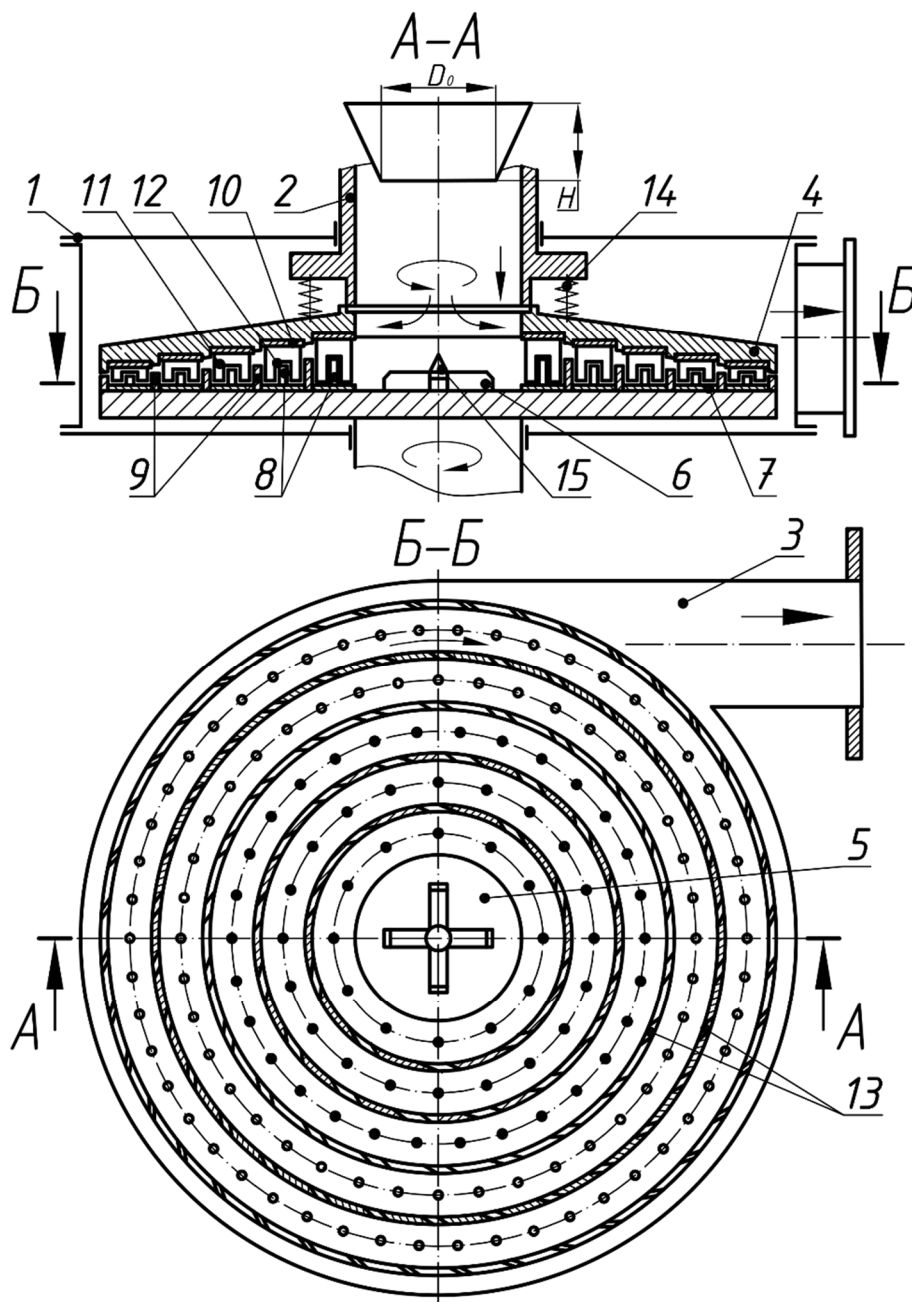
Схема ступенчатой дисковой мельницы: 1 – корпус; 2 – загрузочный патрубок; 3 – разгрузочный патрубок; 4 – верхний диск; 5 – нижний диск; 6 – разбрасыватель; 7 – горизонтальные кольца; 8 – вертикальные штыри; 9 – вертикальные цилиндрические перегородки; 10 – горизонтальные кольца; 11 – радиальные лопасти; 12 – вертикальные вырезы; 13 – тангенциальные вырезы; 14 – пружинная опора; 15 – распределяющий конус
